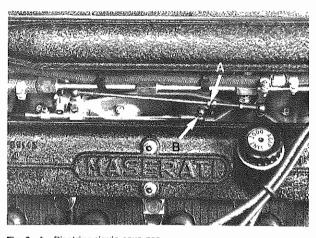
A - Piastrino rinvio cavo gas Throttle cable plate B - Vite regolazione gioco cavo gas Throttle cable adjusting screw
